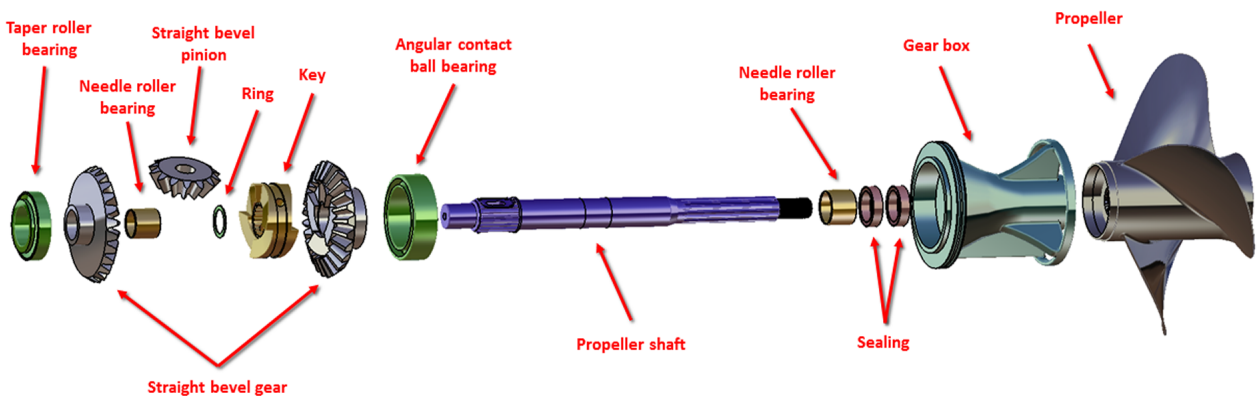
(a)와 Fig. 8(b)는 전기추진용 선외기의 동력전달 축계시스템 구성부품의 개요도를 나타낸다. 미드섹션부의 핵심 구성품인 구동축의 길이는 720mm, 직경은 최대 20mm이며 축 지지용 베어링 2개와 Drive shaft pinion이 연결되어 있다. Drive shaft pinion에 연결되어 있는 Bevel gear는 1개의 Key에 물려 프로펠러축에 동력을 전달해주며 프로펠러축의 길이는 270mm, 직경은 Max. 22mm이며 3개의 베어링에 지지된다. 그 외에 Sealing 2개와 Ring 2개 등이 있다.
